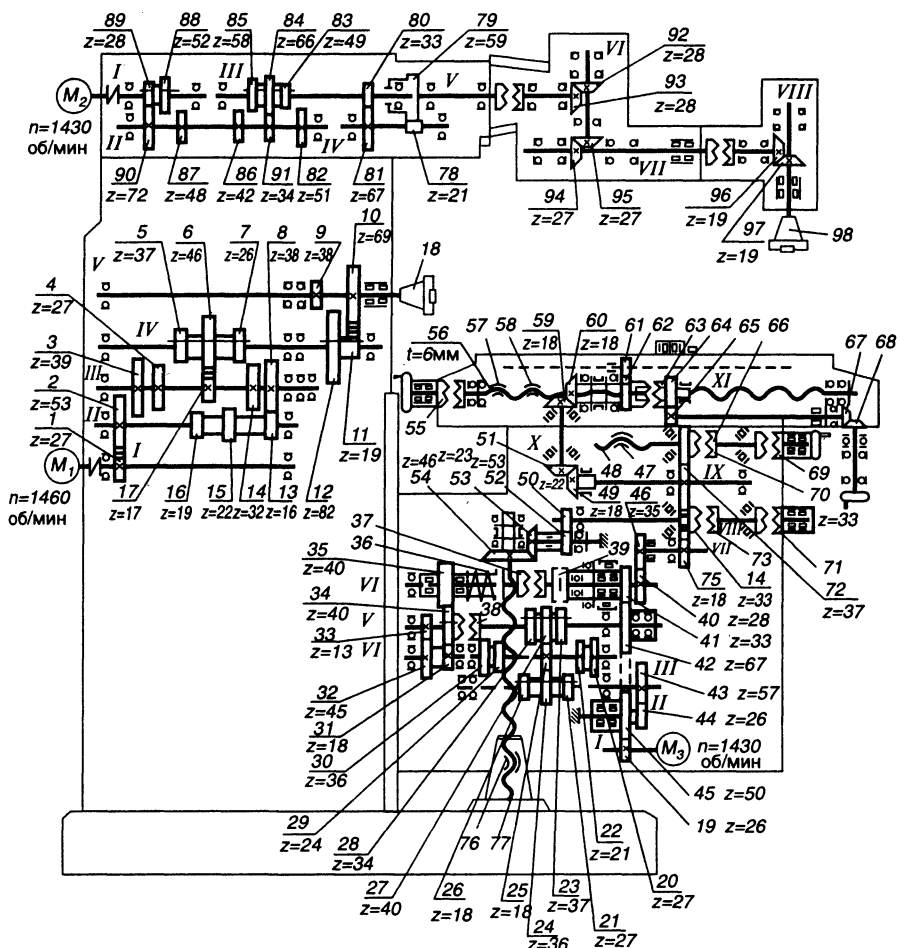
Кинематическая схема станка мод. 6P82Ш:
